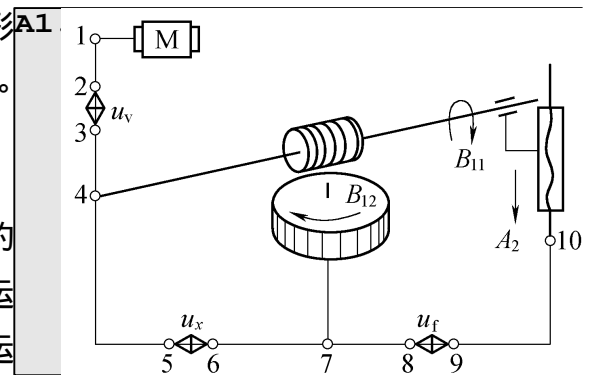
滚切直齿圆柱齿轮的传动原理图
